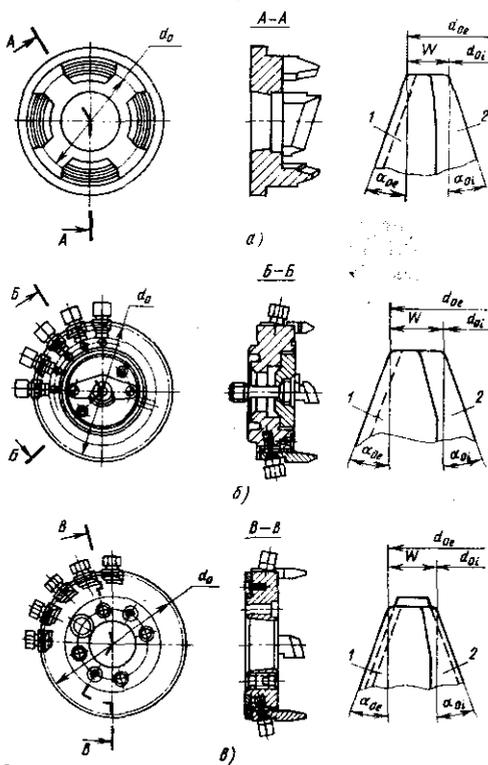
Зуборезные головки: а — цельные; б — сборные чистовые; в — сборные черновые
